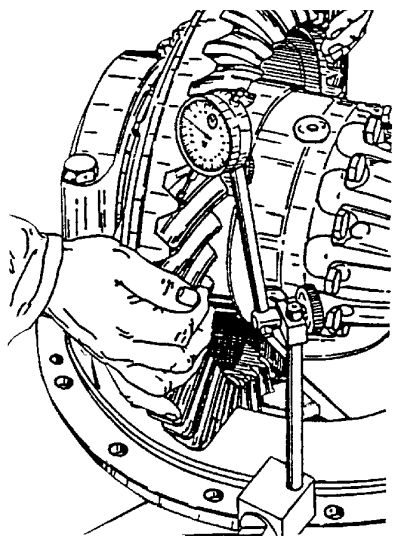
D.15. Проверка зазора в зацеплении зубьев шестерен главной передачи
